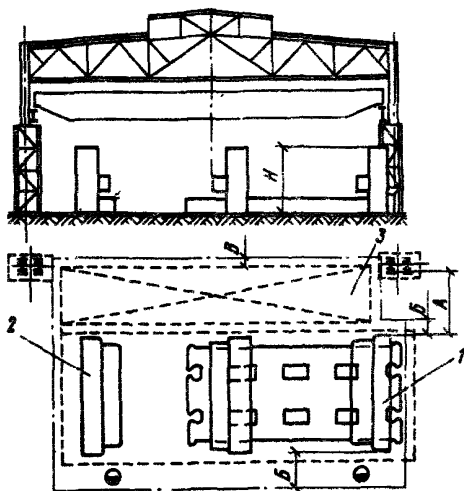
Размещение двухстороннего торцефрезерного станка в поперечном пролете
